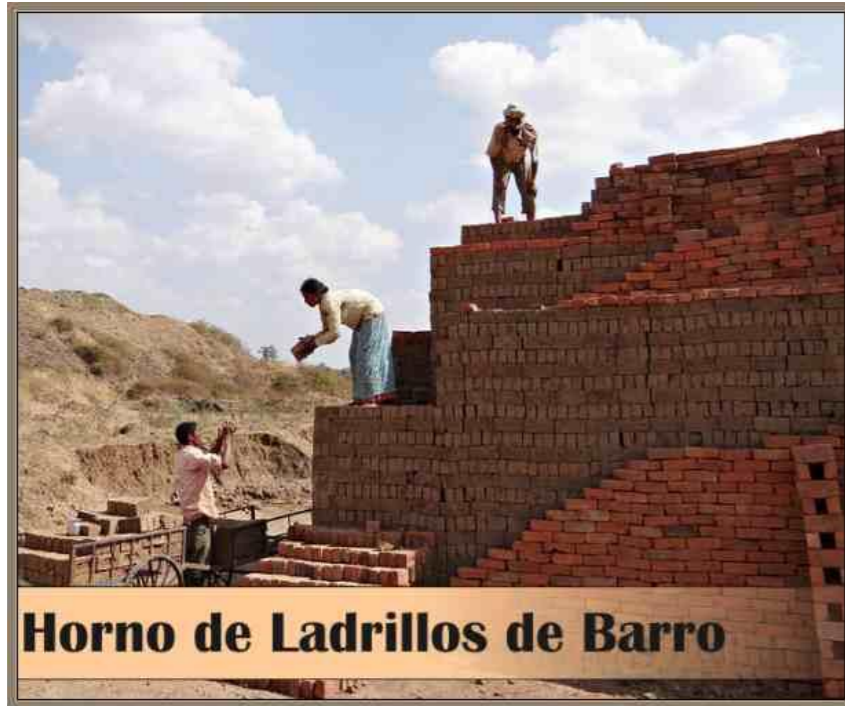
Hornos y manufactura de elemento constructivo más usado en el tiempo de los inicios de construcción.
